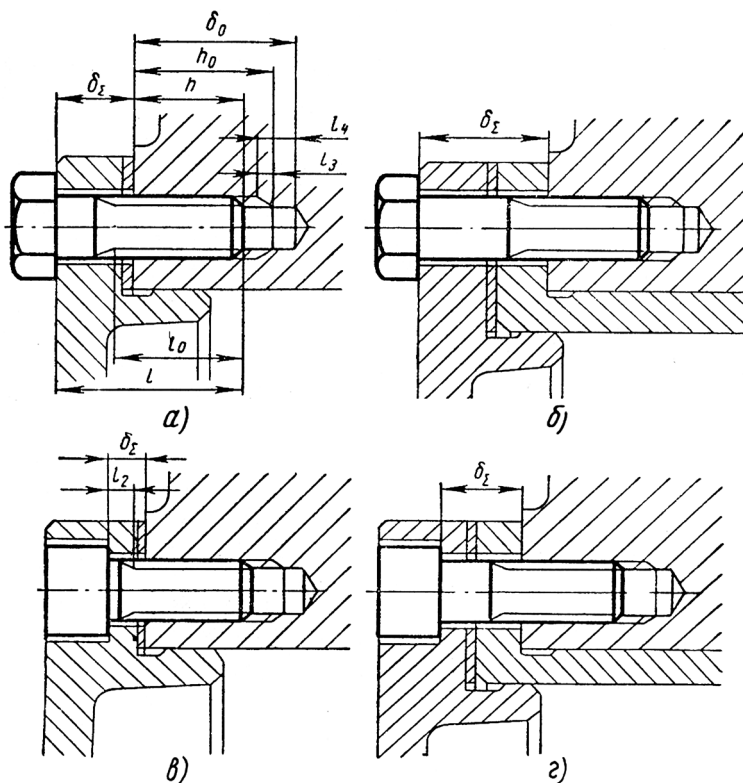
Крепление крышек подшипников (а, в) и крепление крышек подшипников со стаканами (б, г) к корпусным деталям
